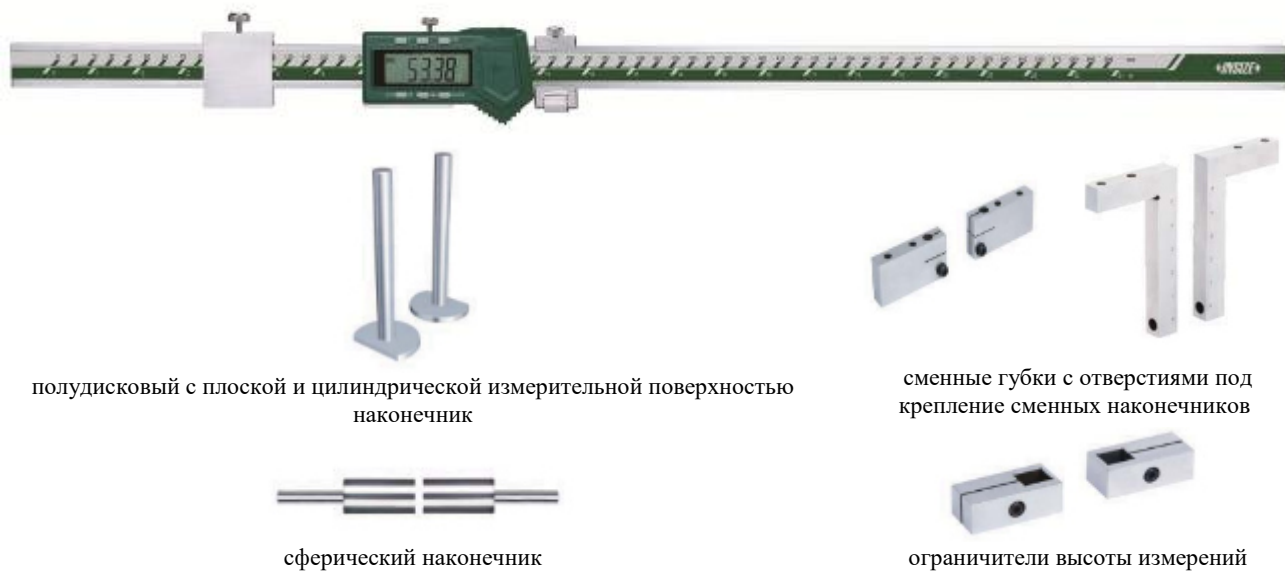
Общий вид штангенциркулей модификации 1125 исполнений 600, 1000, 600WL, 1000WL
